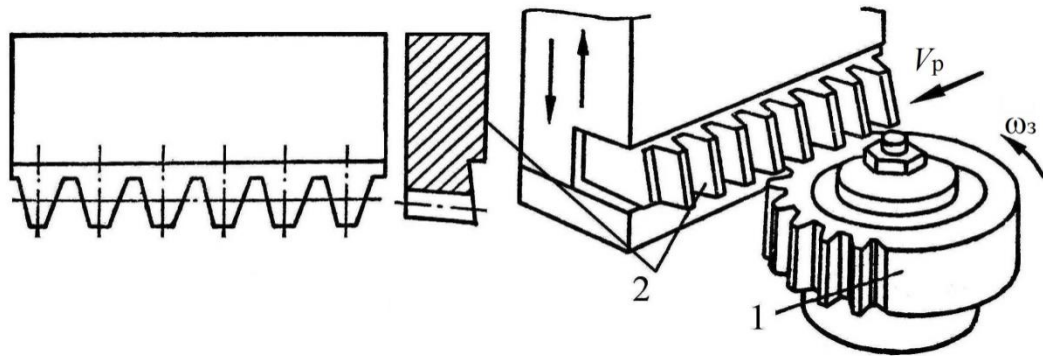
Нарізування зубчастого колеса рейкою (виробляючим контуром)
